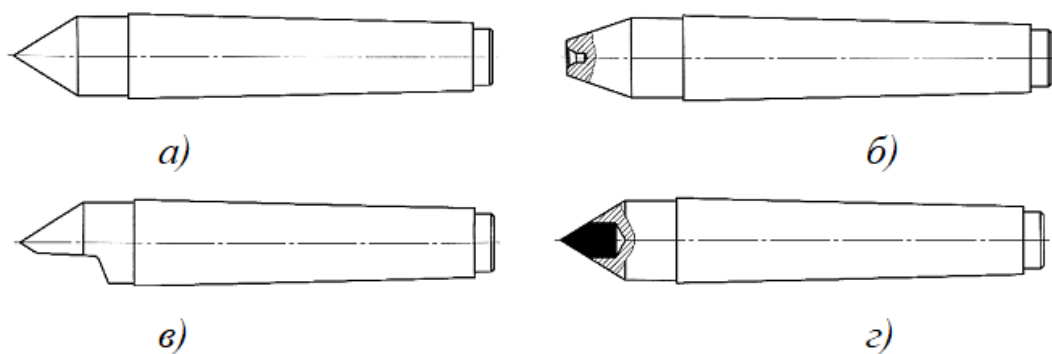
Типи необертових задніх центрів: а) твердий центр; б) зворотний центр; в) напівцентр; г) твердосплавний центр.
